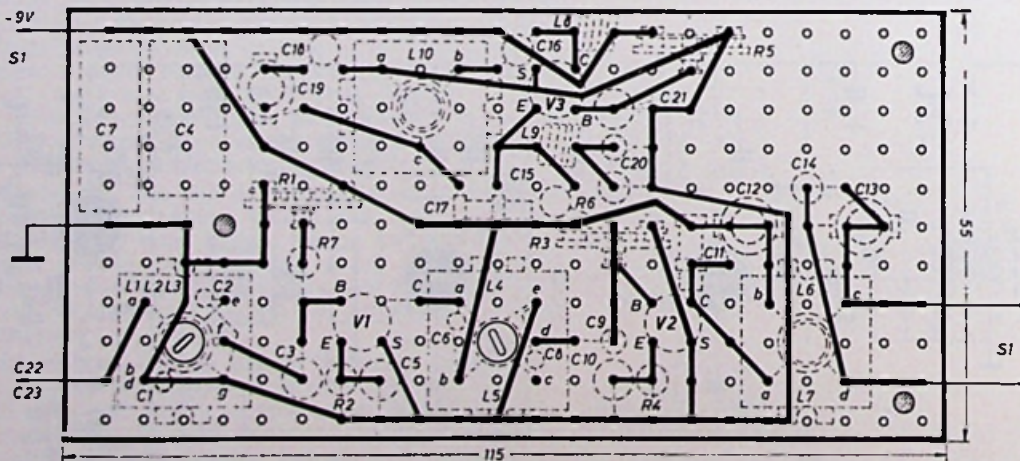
Bedradingsvoorbeeld voor de montageplaat (onderaanzicht).
